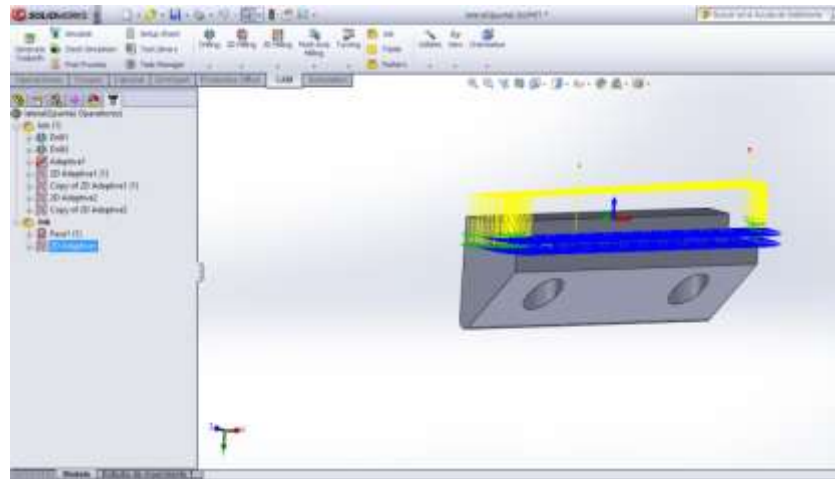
8 Diseño CAM de puntas (maquinado de escalón)
